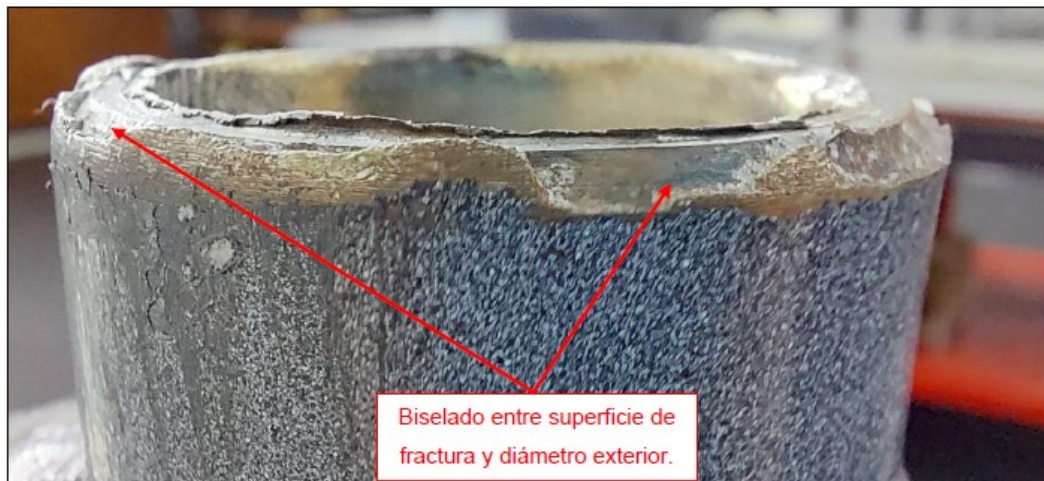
Biselado en la zona de fractura - imagen A. Fuente: investigación JST
